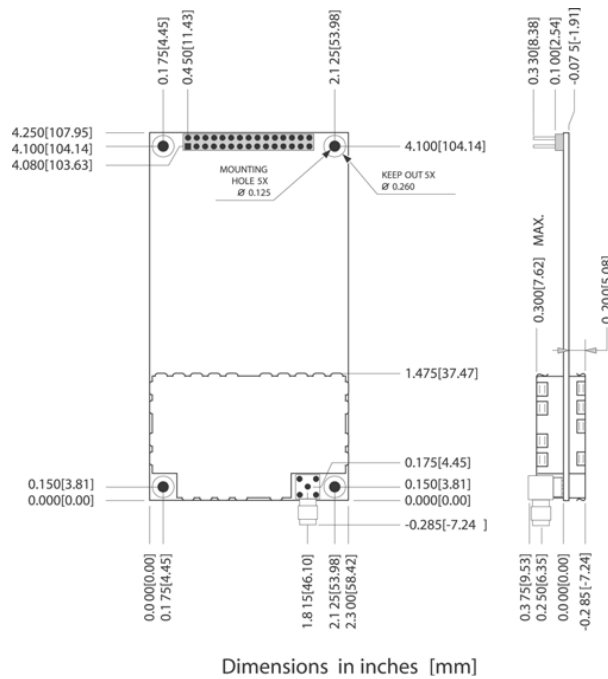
Dimensiones del receptor GPS DG14 Board
